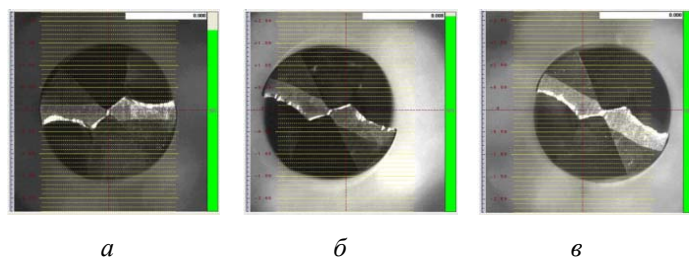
Характер износа режущей кромки инструмента при сверлении:
